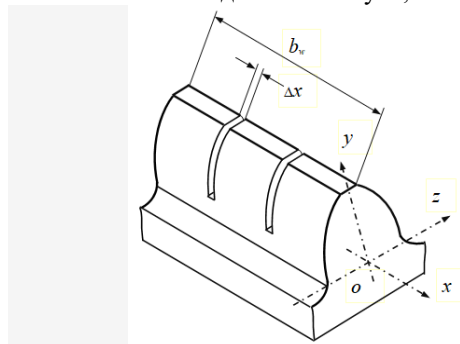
Зуб зубчатого колеса с кольцевыми канавками
